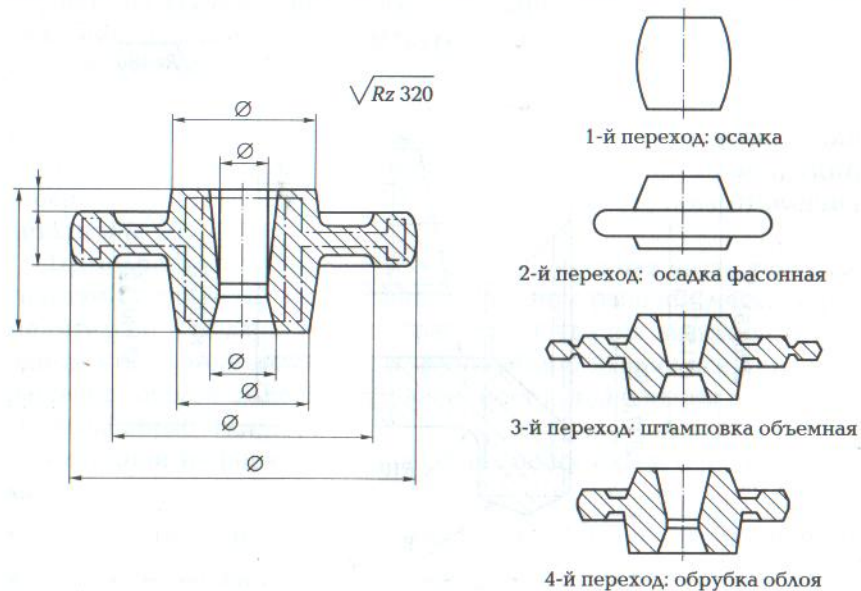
Заготовка — штамповка и последовательность ее изготовления
